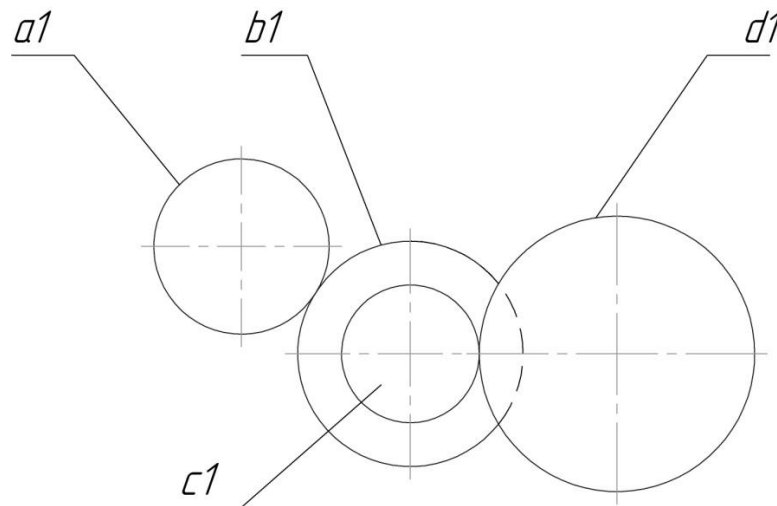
Ескіз гітари подачі зубофрезерного верстата
